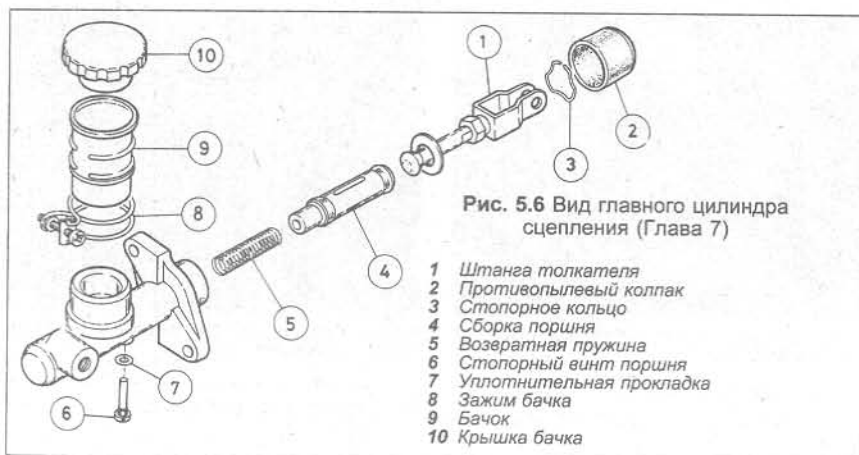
Вид главного цилиндра сцепления (Глава 7)
